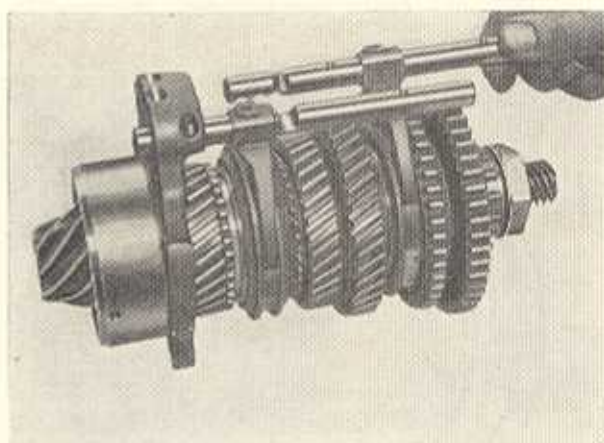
Schaltstange für 1. und 2. Gang einführen
